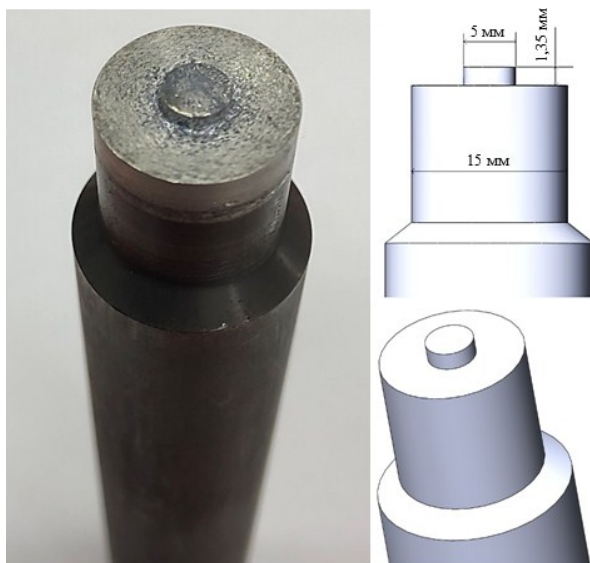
Инструмент для сварки трением с перемешиванием
